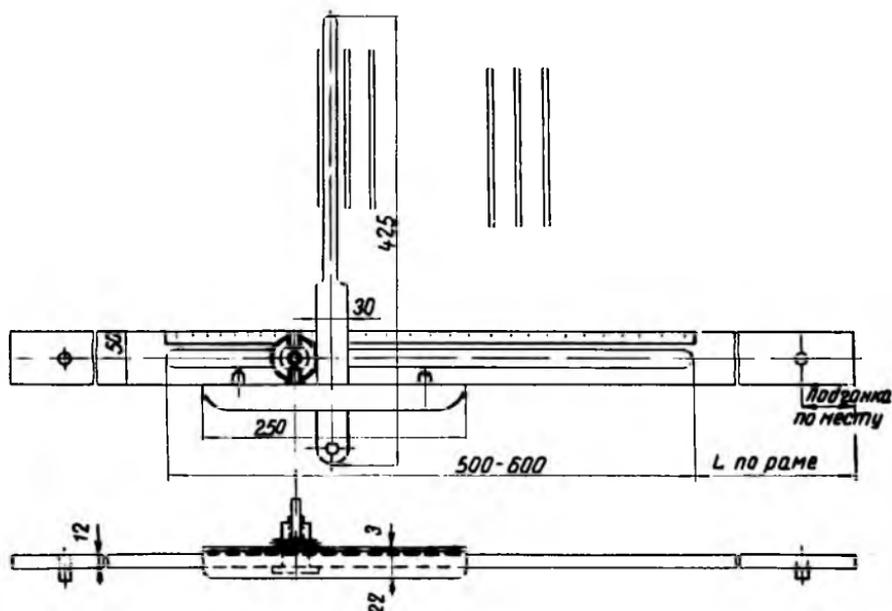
Выверочная линейка и угольник для проверки положения рамных пил
